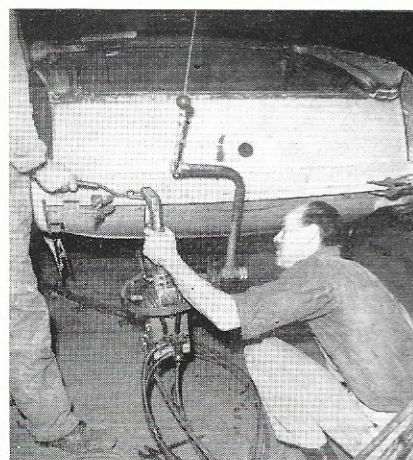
Soudage du panneau arrière sur tôle bavolet et traverse. Pour éviter de marquer la tôle, interposer une palette entre celle-ci et l'électrode.
